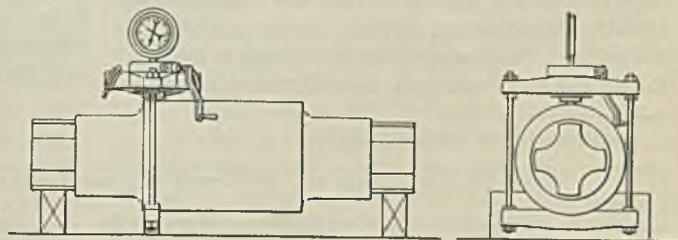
Apparat zur Kugeldruckprobe bei Walzen.
